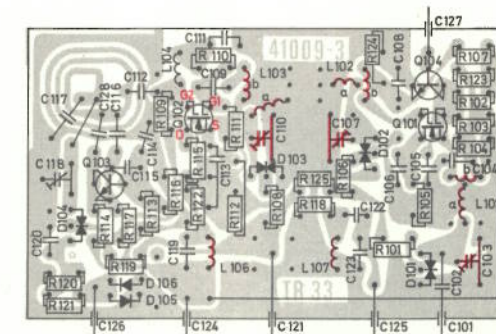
FM-tuner plate med symb. komp. plassering sett fra loddessiden.
